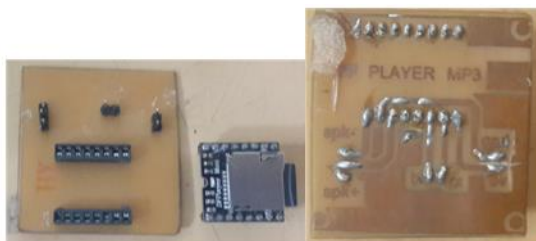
Placa del sistema de audio vista frontal y pistas soldadas vista posterior
